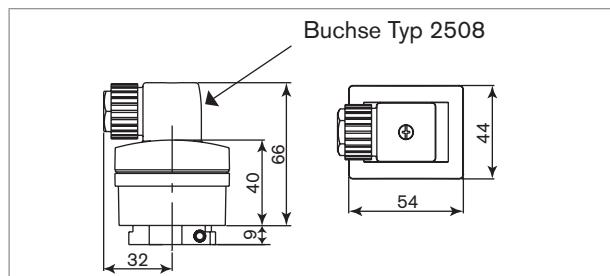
Abmessungen [mm] des Elektronikmoduls SE30 Ex
